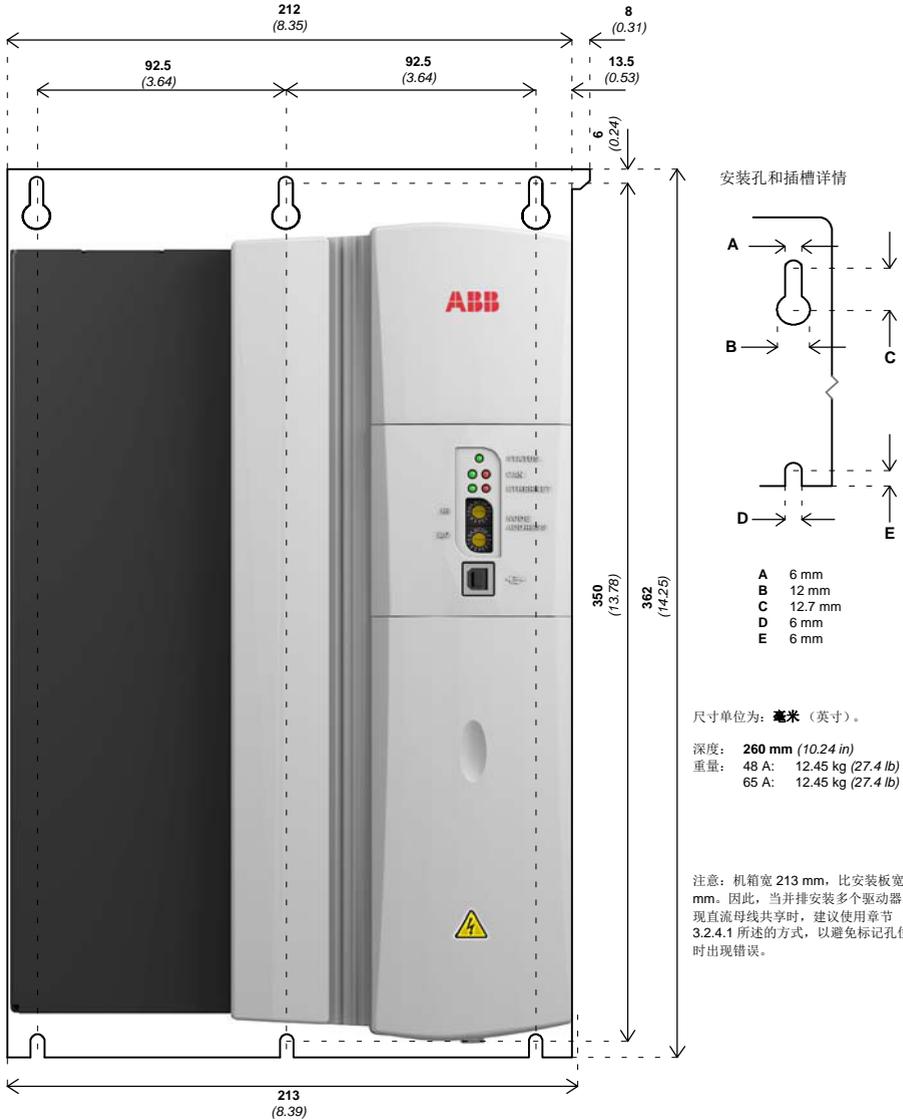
：安装尺寸和总体尺寸 - 48 A ~ 65 A 型
